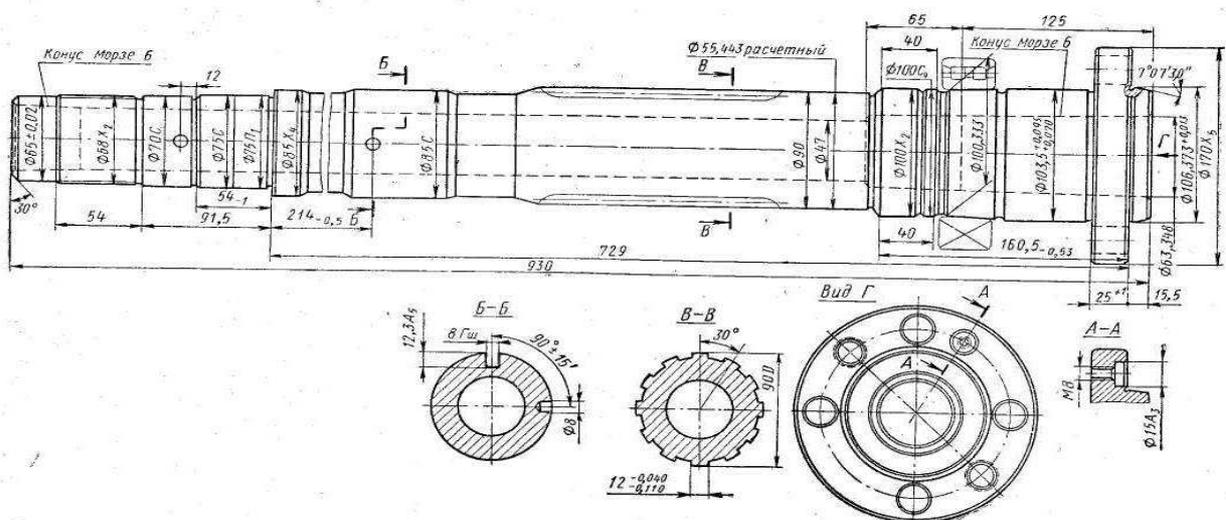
Шпиндель токарного станка (рабочий чертеж)
